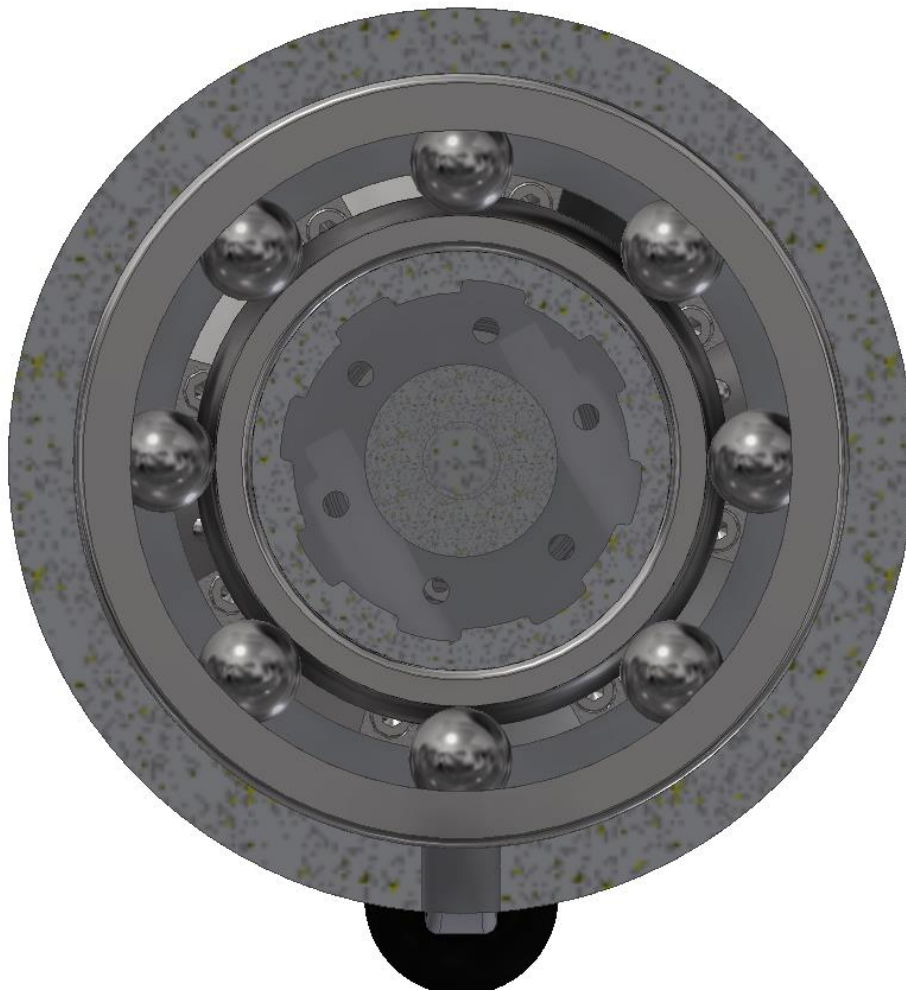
З'єднання коронка – гайка ролико-гвинтової подачі.
